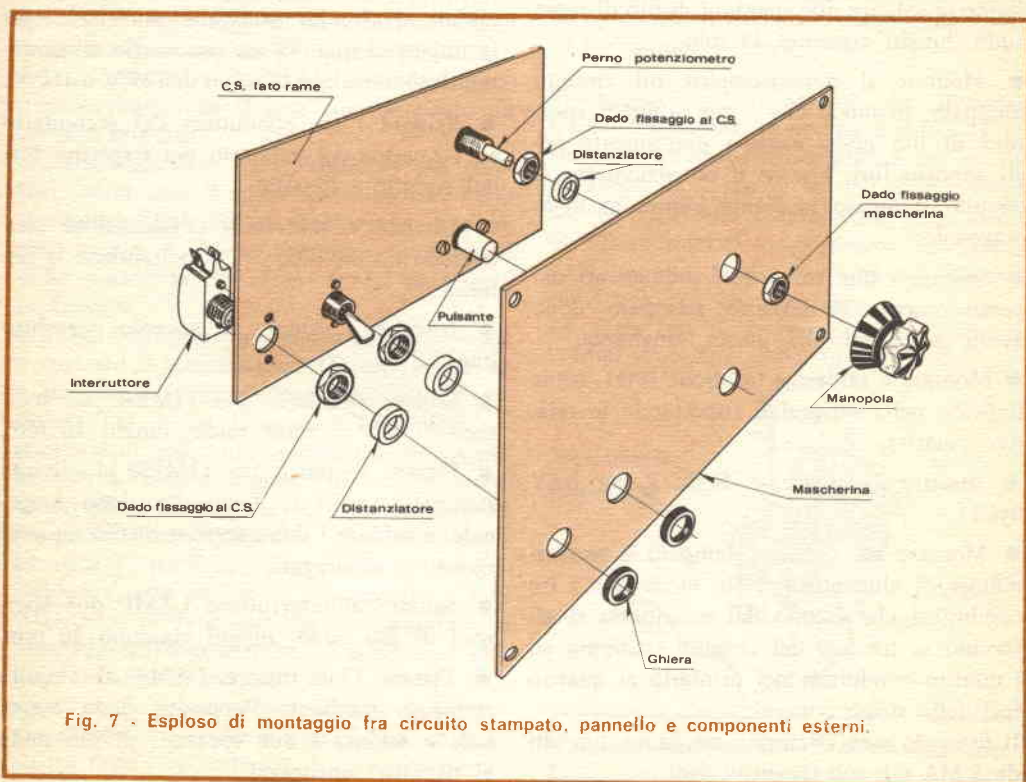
Esploso di montaggio fra circuito stampato, pannello e componenti esterni.
